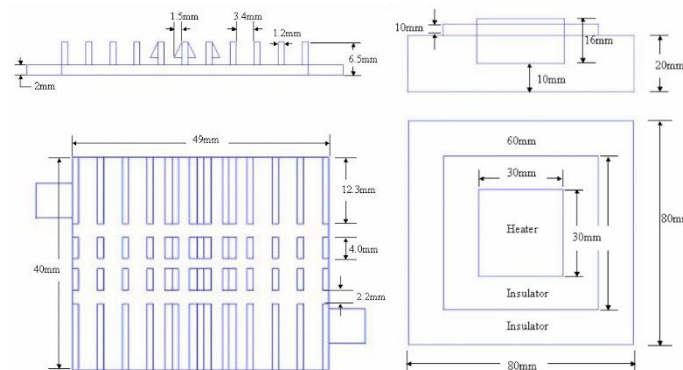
北橋 Heat Sink 幾何結構與加熱片尺寸
